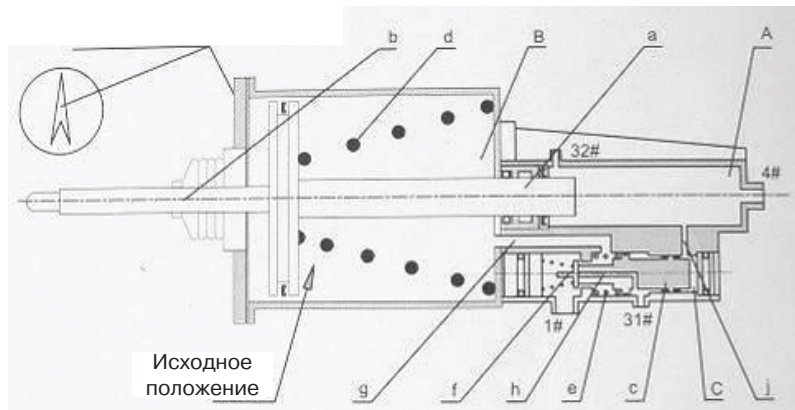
Схематический чертеж сервоусилителя сцепления
